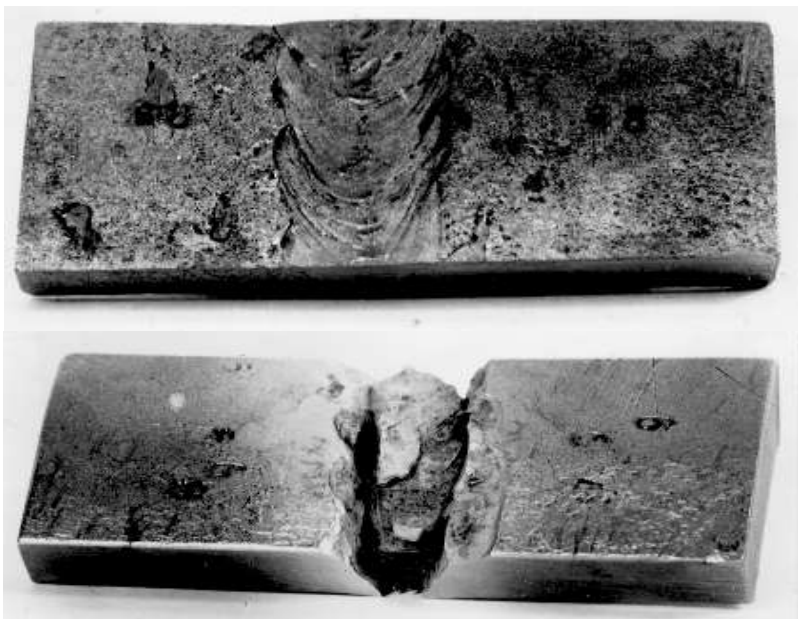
Зовнішній вигляд зразків зварного з'єднання зі сталі 12X18H10T
